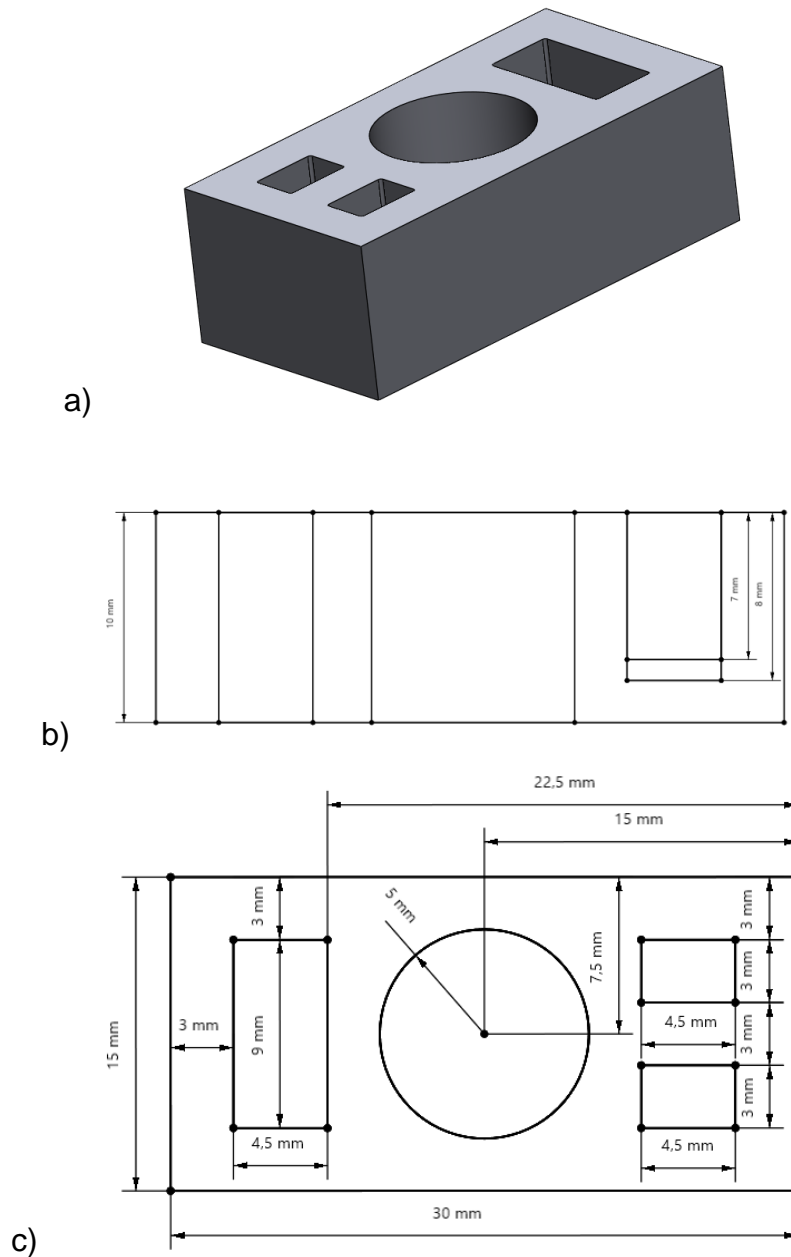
a) Imagen de la pieza 1 extraída del software Geomagic Design X; b) Imagen de las dimensiones geométricas de la pieza 1 en alzado; c) Imagen de las dimensiones geométricas de la pieza 1 en planta.
